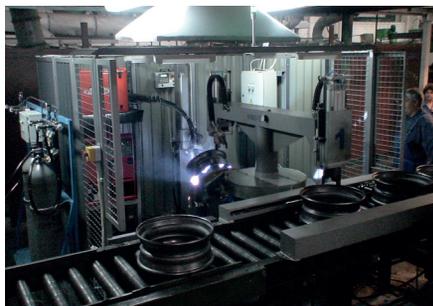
Конвейер АС363 для двухдуговой МИГ-сварки обода с диском автомобильных колес
